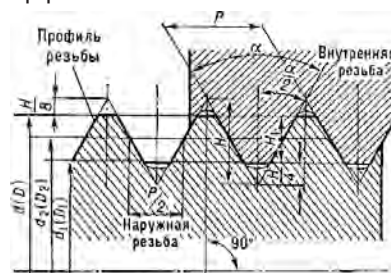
Схематическое изображение стандартного соединения «шпилька-гайка»
